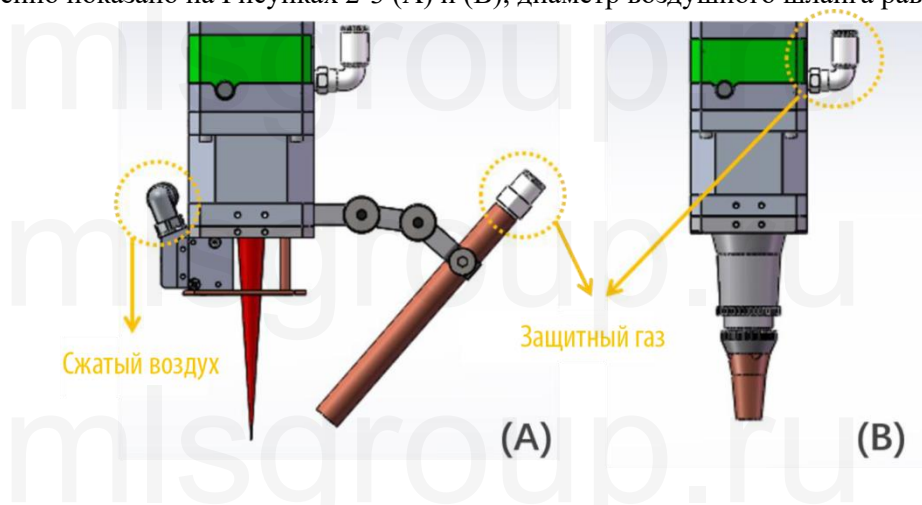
Подключение пневматической линии лазерной сварочной головки с двойным диапазоном BW290
